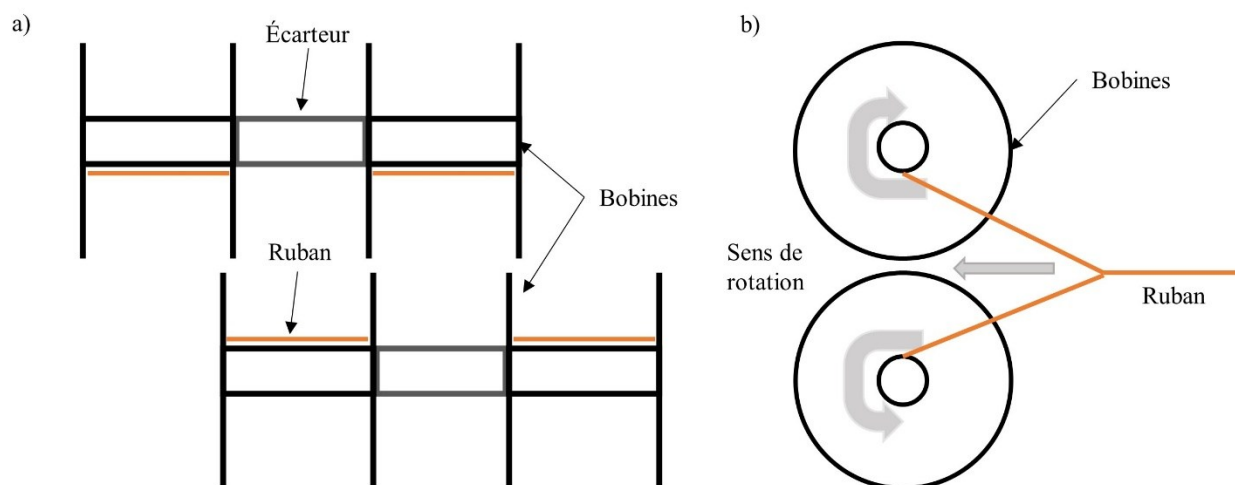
Système de bobinage: a) vue de face des bobines, b) vue de côté
